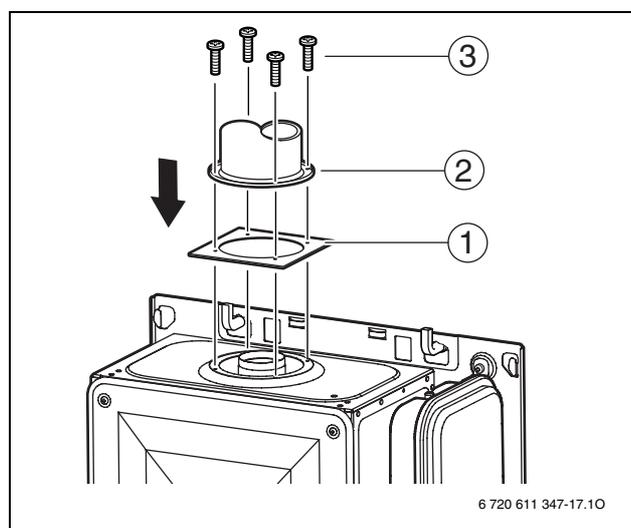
Fissaggio dell'accessorio per gas combusti (esempio Ø 80 mm)
